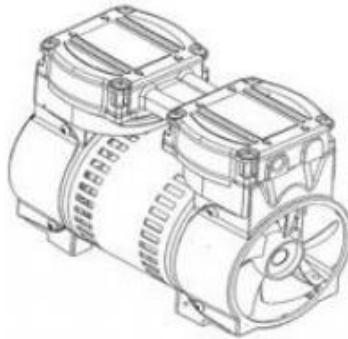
Compresor de Baja Presión, Fuente: (Diseño Propio)
